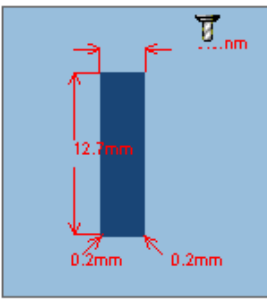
Ріжуча пластинка «266RG-22TR01F600E 1020»
